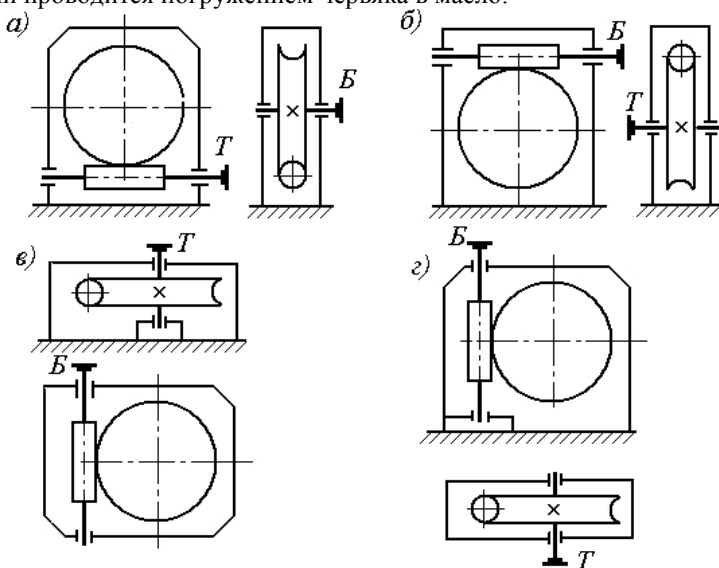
Кинематические схемы одноступенчатых червячных редукторов
